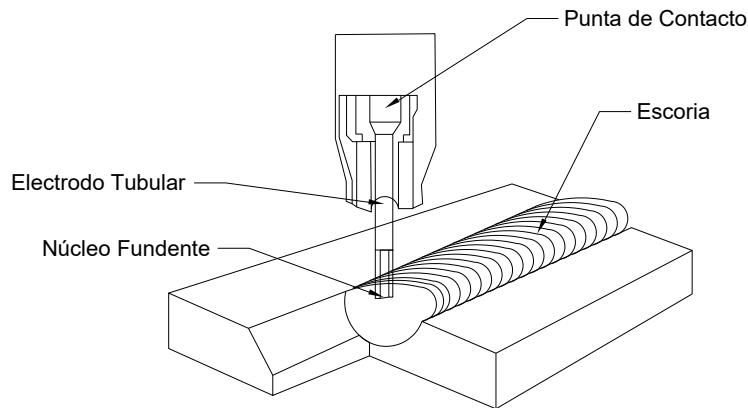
Proceso para la soldadura FCAW.
